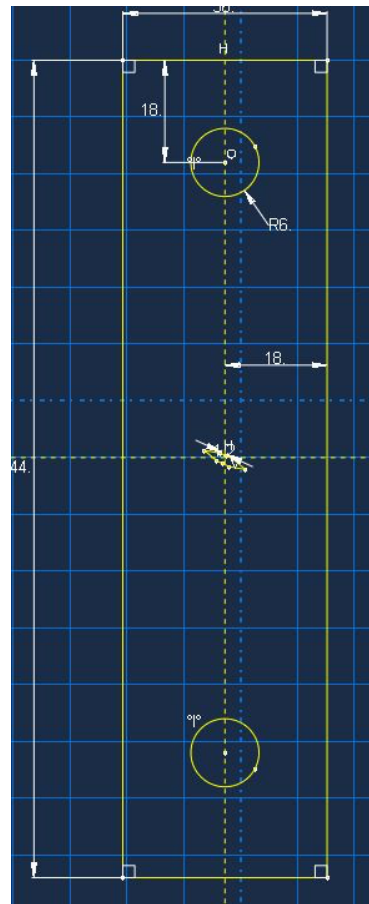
Geometría de probeta MT con grieta central inclinada.
